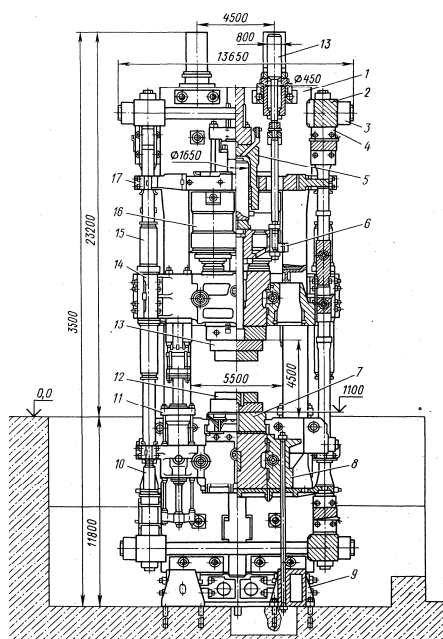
Общий вид штамповочного гидравлического пресса усилием 650 МН
